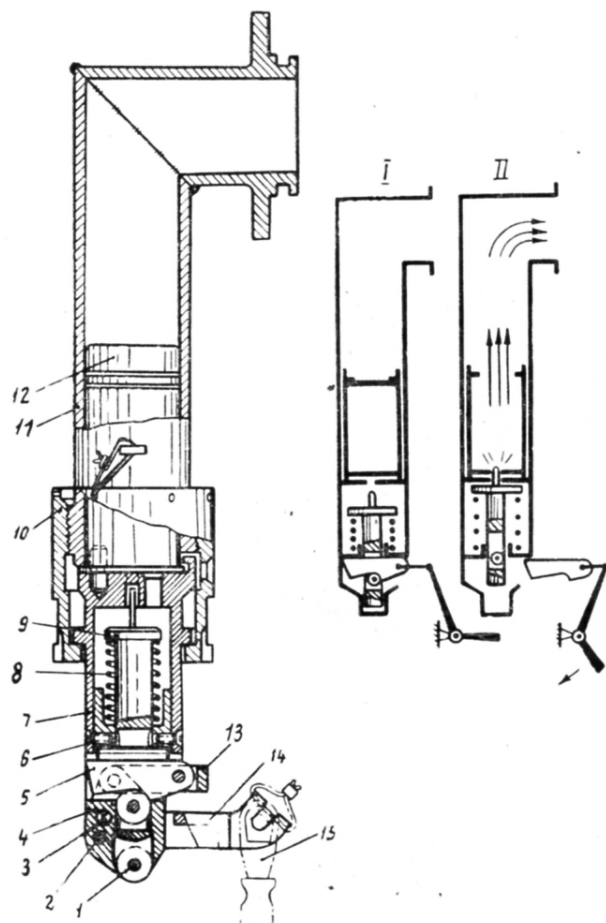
Воспламенитель порохового заряда ускорителя: 1—ось; 2—срезной винт (показан условно); 3—наземный стопор; 4—головка затвора; 5—чека; 6—винт; 7—корпус затвора; 8—пружина; 9—ударник; 10—накидная гайка; 11—корпус; 12—патрон ПВ-50; 13—поводок; 14—качалка; 15—наконечник троса
